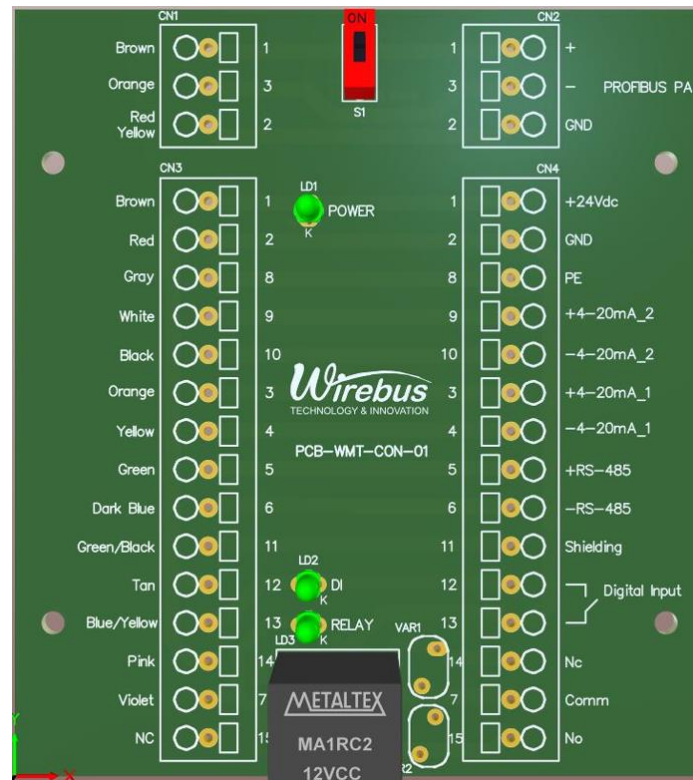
Caixa de Passagem - Borneira de Conexão Placa Interna
